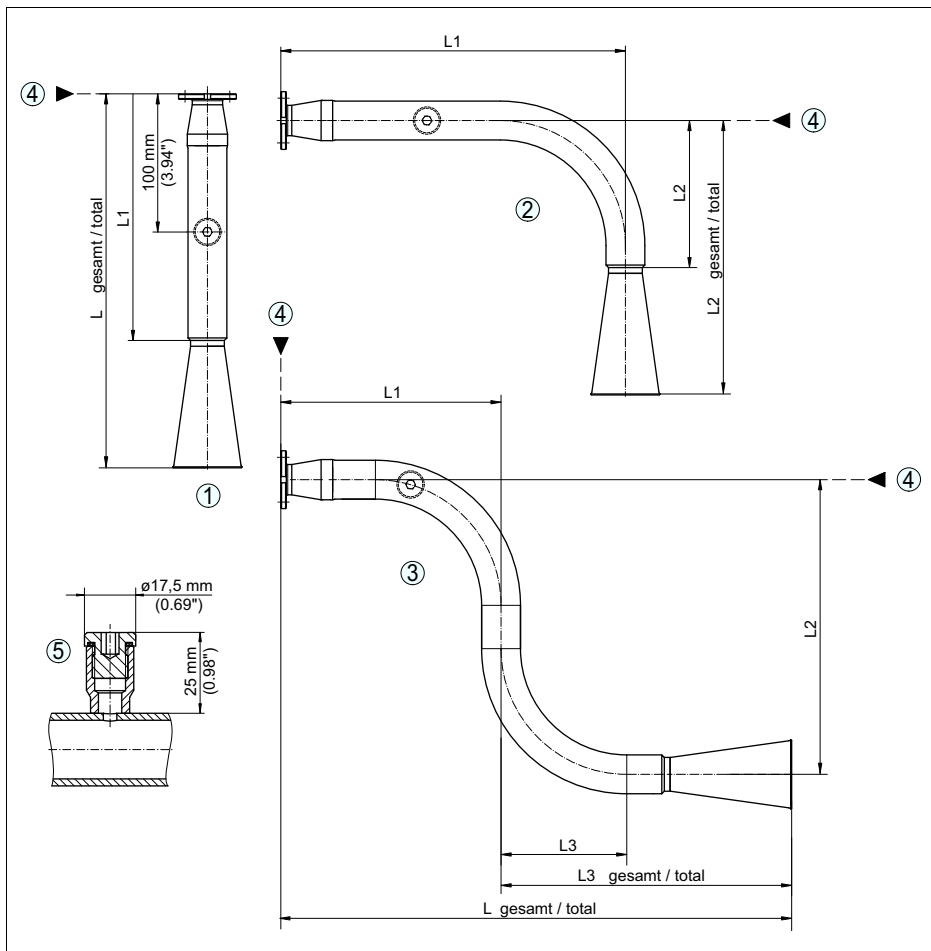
Prolongación uniseccional, con antena de trompeta soldada, medidas según la especificación de pedido
